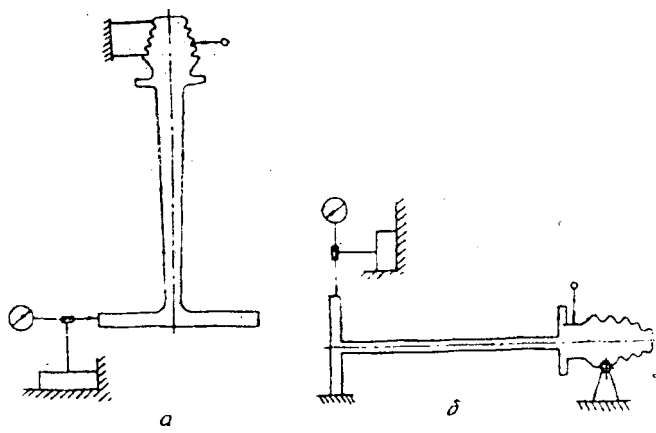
Схемы контроля контура бандажной полки лопатки турбины. а -- со стороны корыта; б -- со стороны спинки
